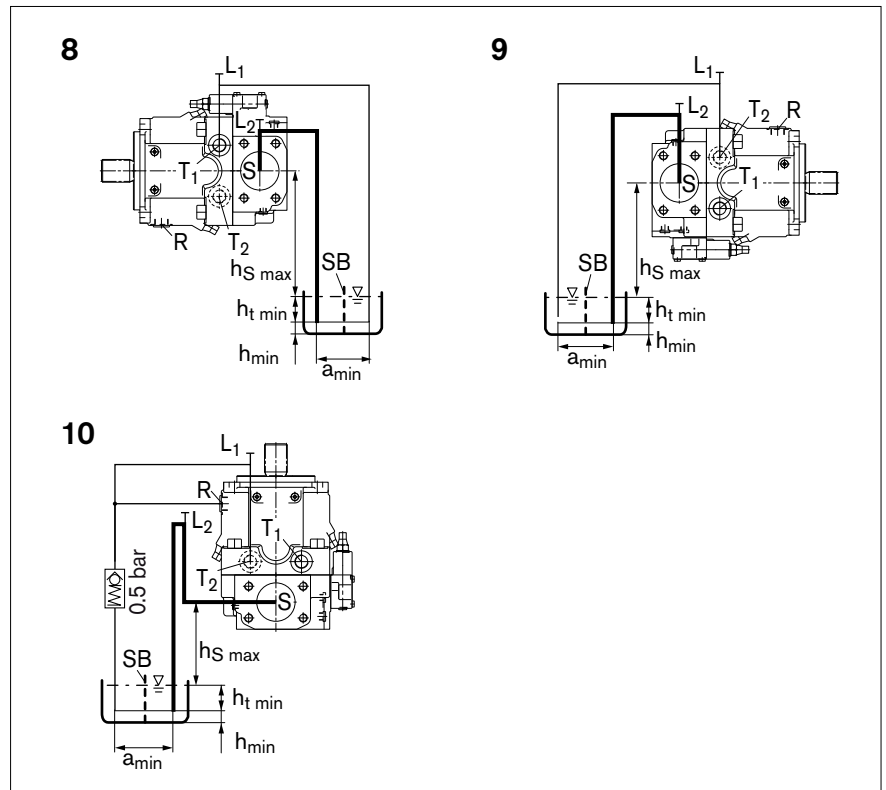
Übertankeinbau mit Einbaulage 8–10
